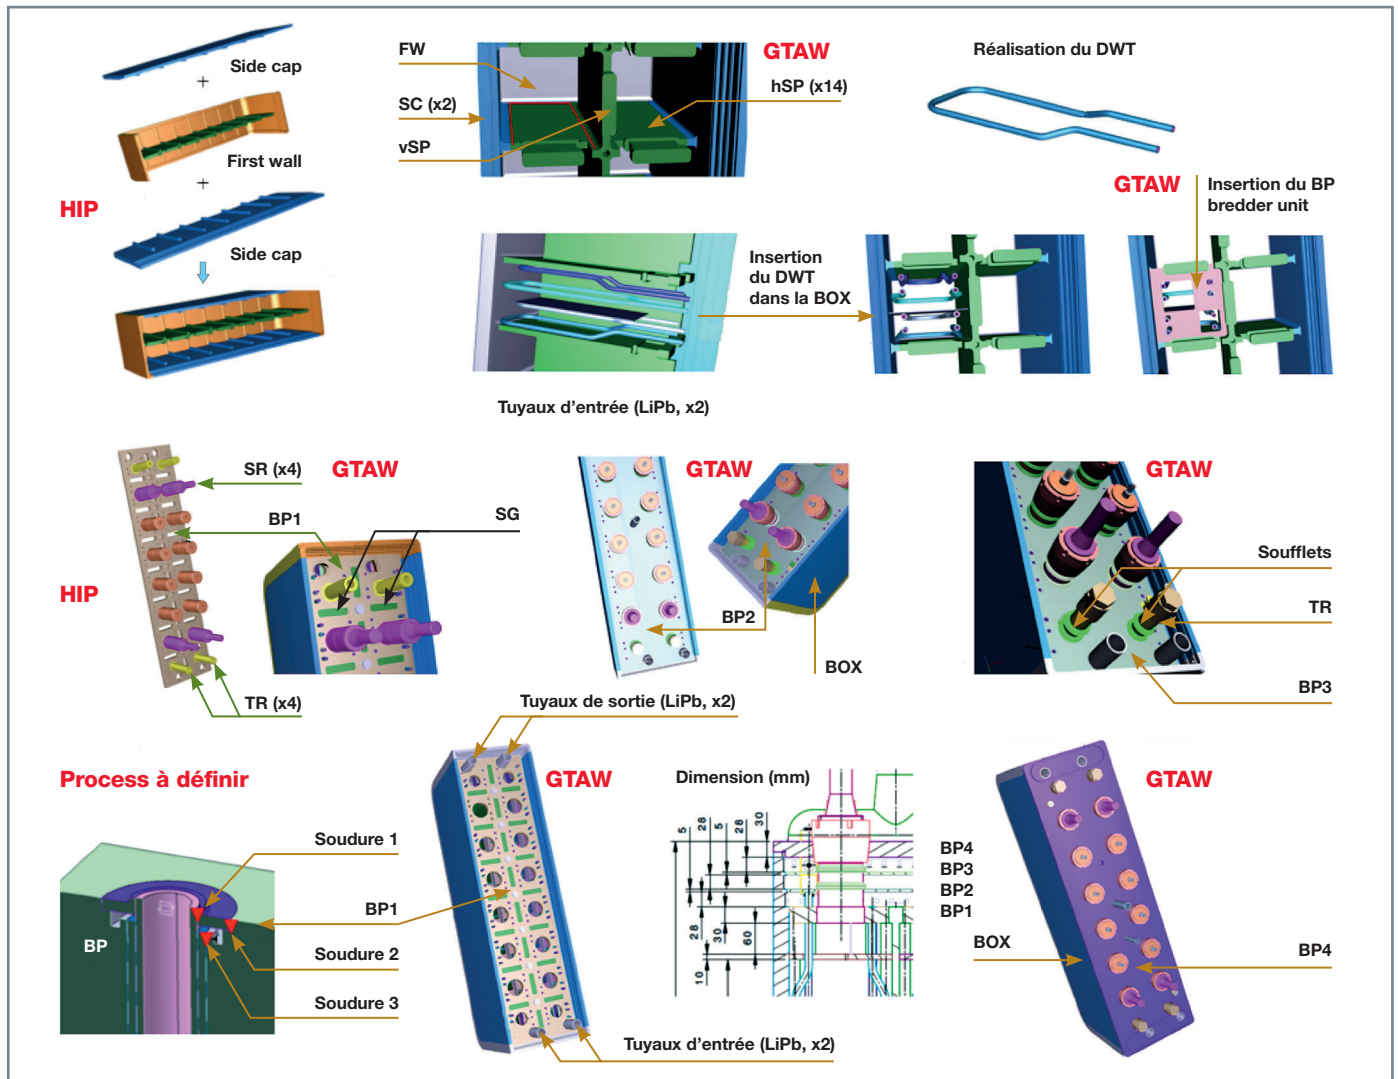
Illustration des principales étapes de soudage du concept WCLL TBM. Les sous-composants à assembler sont indiqués en noir et les procédés de soudage en rouge.
